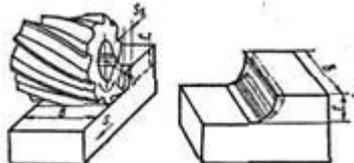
Фрезерование цилиндрической винтовой фрезой: B — ширина фрезерования, t — глубина фрезерования, s — наибольшая толщина среза
